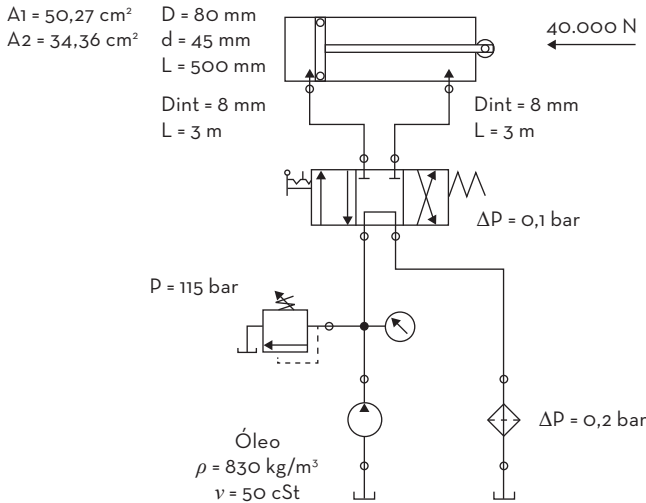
Esquema hidráulico da máquina de dobragem de tubos
